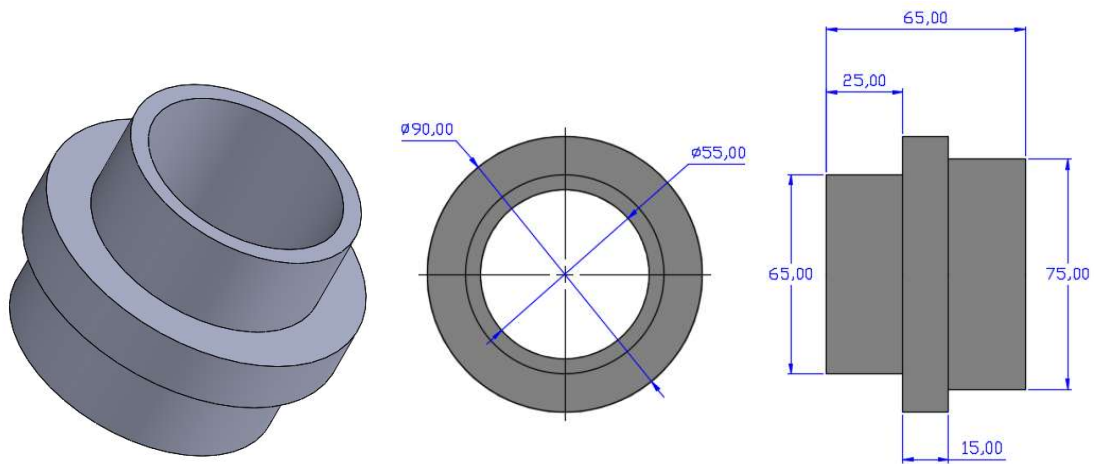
Vista 3D y dimensiones de la pieza mecanizada para transmitir fuerza axial.
